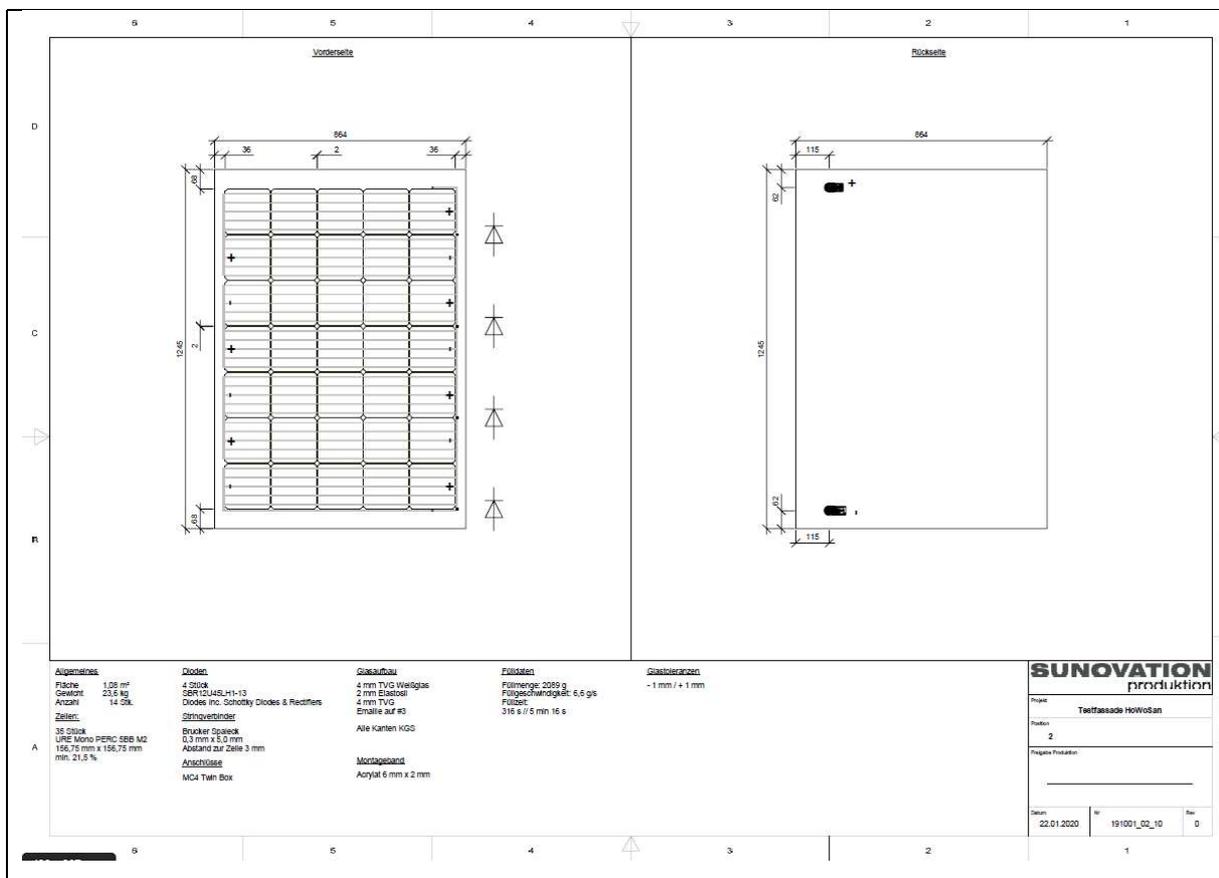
Fertigungszeichnung der PV Module für die Testfassade in Kassel: Position 2.
